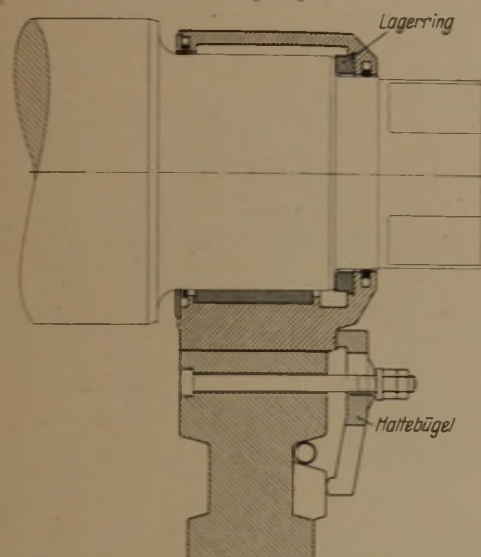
Walzenlager geschlossen mit Axiallagerung.
